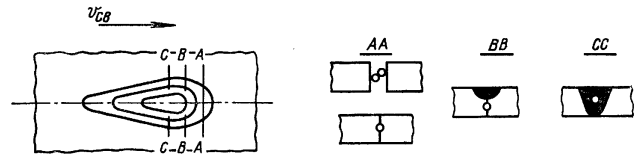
Схема образования пор при сварке встык алюминиевых сплавов
